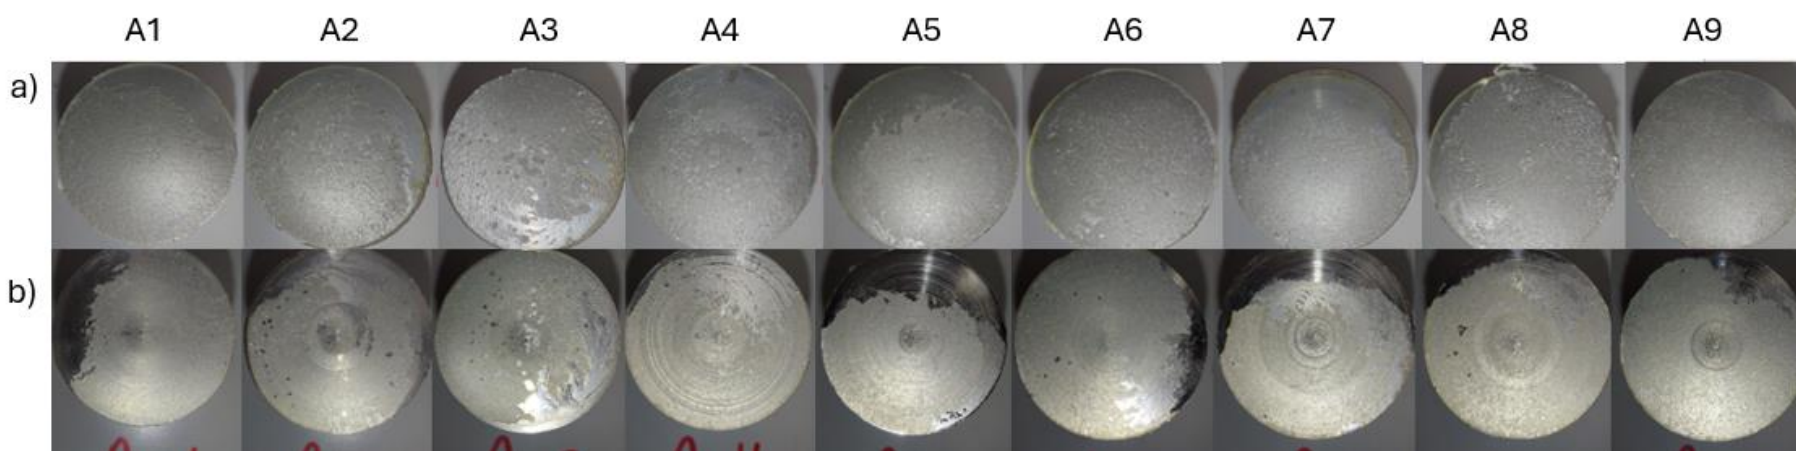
Muestras del ensayo TAT en duplicado; a) Piezas recubiertas b) Piezas de sustrato
